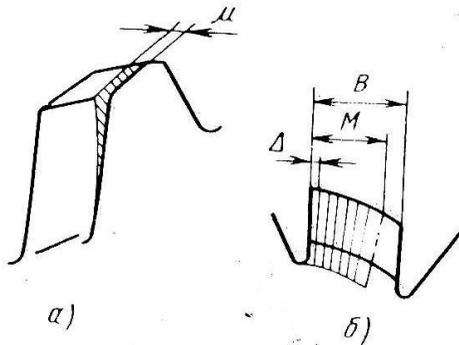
Изнашивание зубьев червячной фрезы: а) характер изнашивания; б) схема заточки
